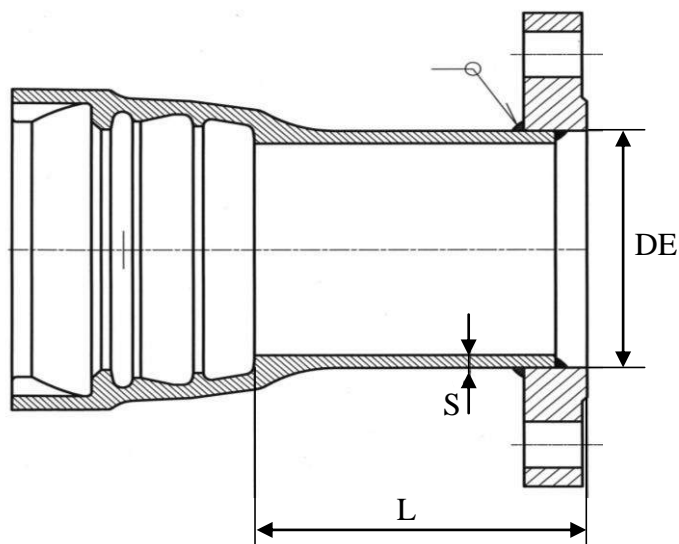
Патрубок фланец – гладкий конец (расположение сварного шва зависит от вида фланца)
